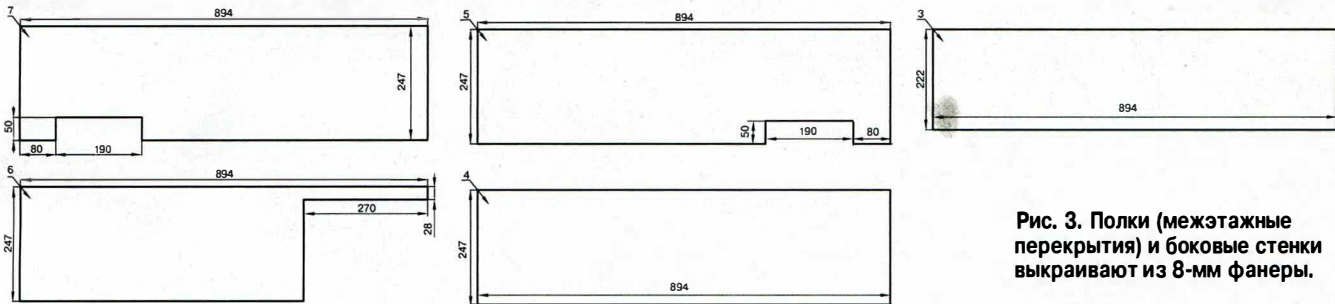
Полки (межэтажные перекрытия) и боковые стенки выкраивают из 8-мм фанеры.
